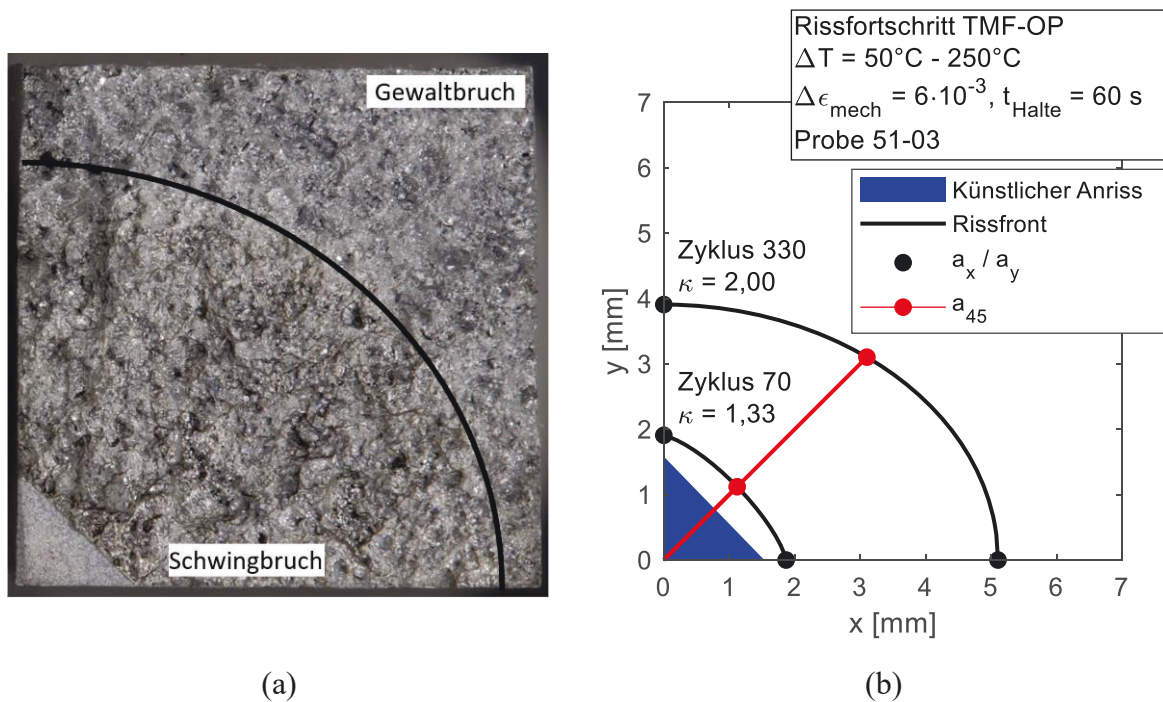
(a) Bruchfläche einer Corner-Crack-Probe (Probe 51-02) mit künstlichem Anriss, Schwing- und Gewaltbruchbereich und (b) Modellierung des künstlichen Anrisses und der Rissfront sowie berechnete Risslänge  $a_{45}$  (Probe 51-03).
